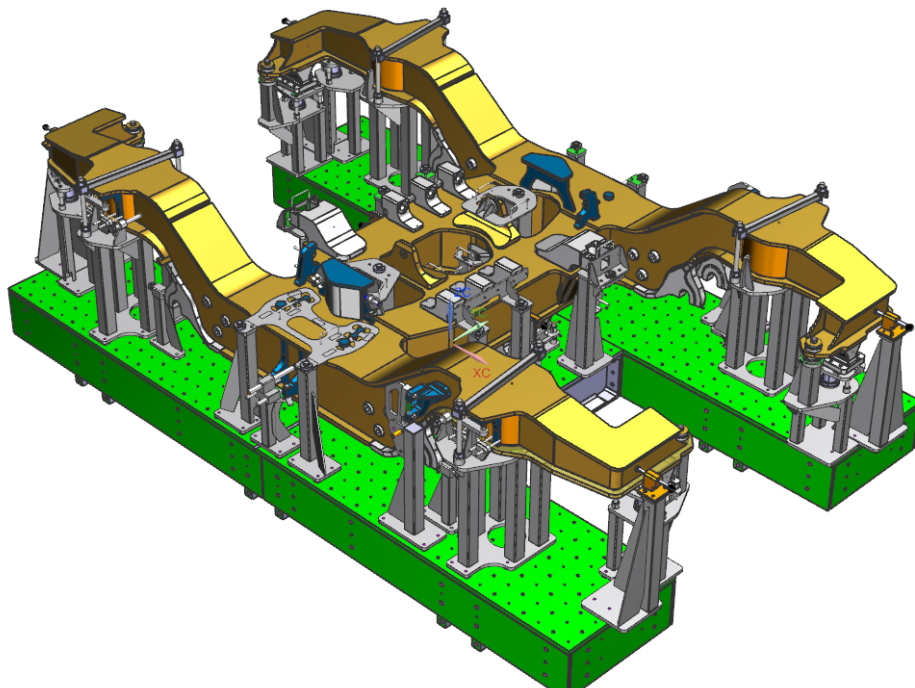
Ejemplo de útil para montar soportes soldados en el bastidor.
